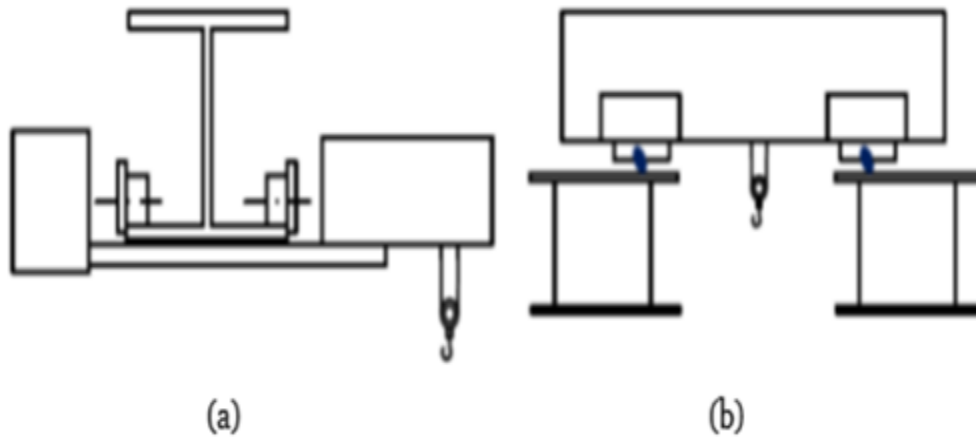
Pont roulant avec: (a)mono poutre,(b)bipoutres
